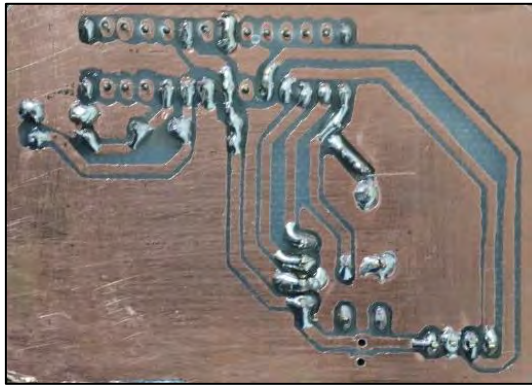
Imagen de las pistas ya soldadas con los pines de los componentes.
